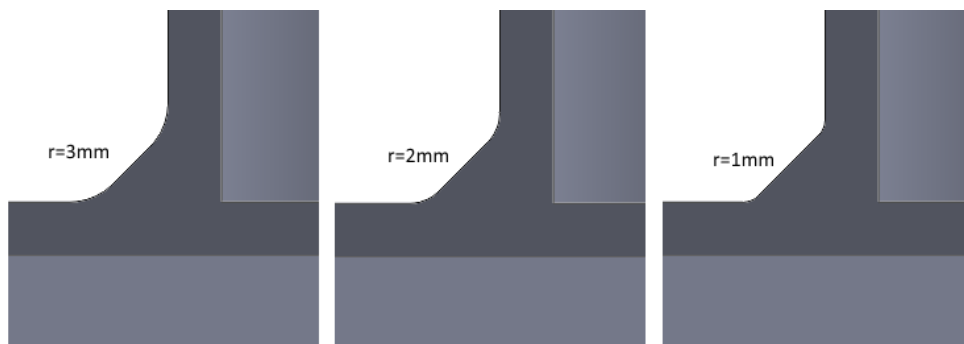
Geometria da soldadura para os diferentes raios testados
